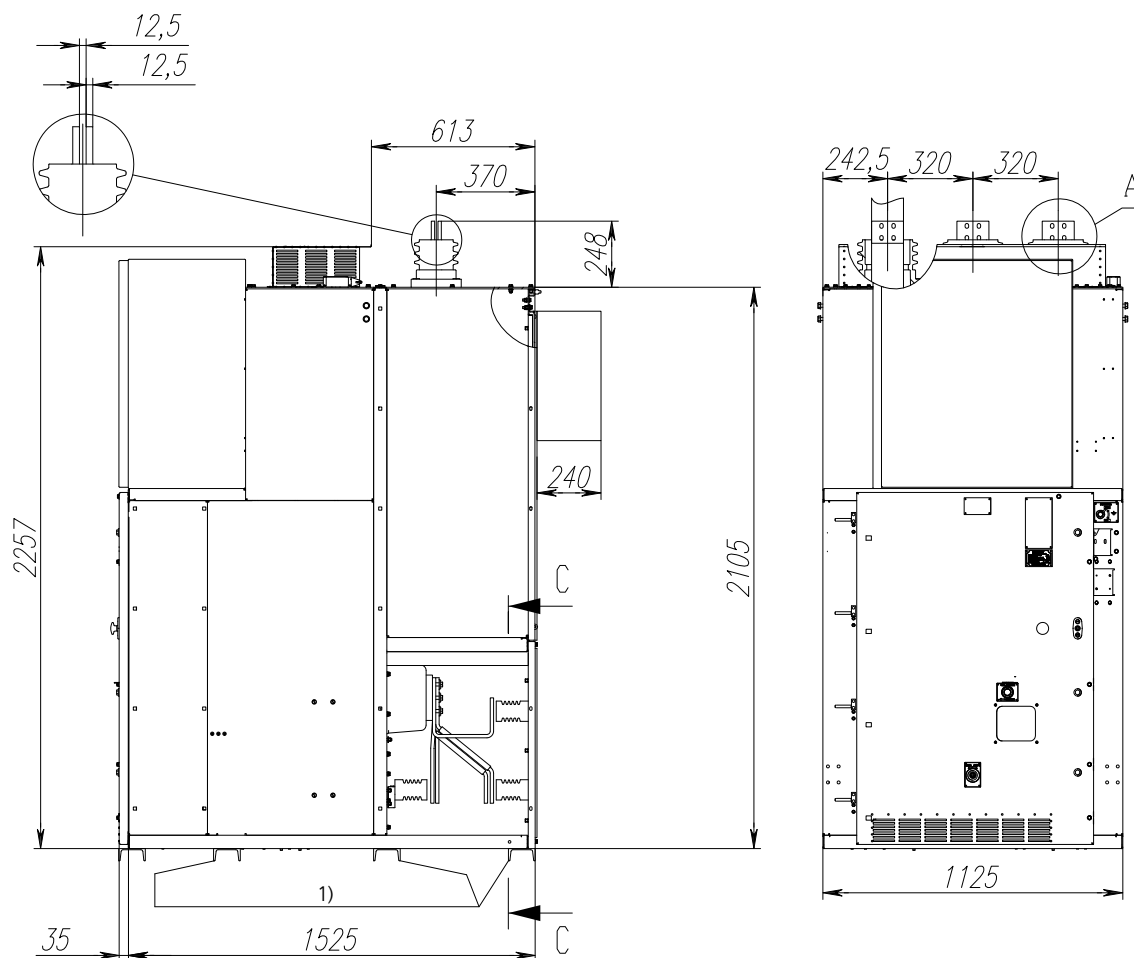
Общий вид и габаритные размеры шкафа К-128 шинного ввода с ТН до ввода на номинальные токи 2000-4000 А
